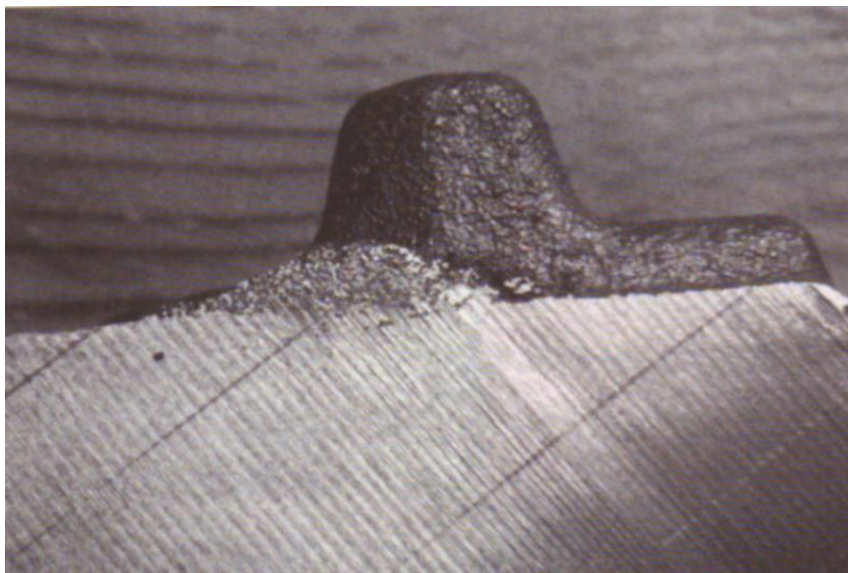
Exploze v dutině formy nad stoupající hladinou tekutého kovu [13]
